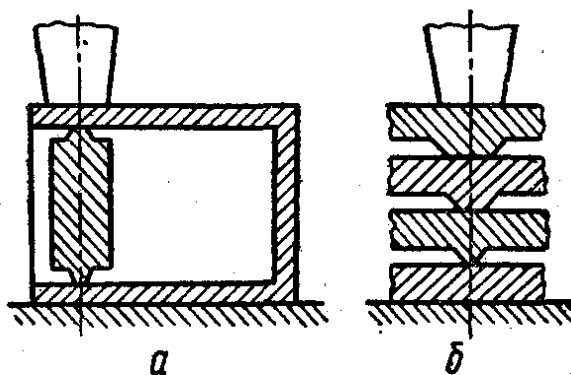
Приклад обробки кромки деталі прямокутного перерізу, що приварюється до тонкостінної камери, і зварювального пакета з декількох пластин.
